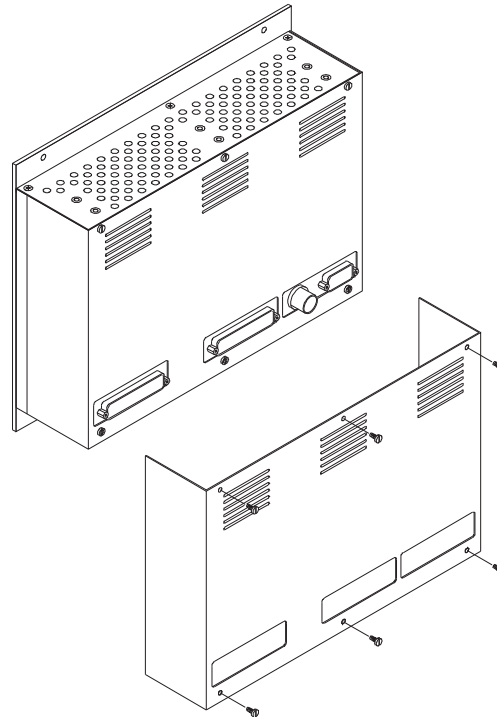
Montieren des rückseitigen Abdeckbleches
